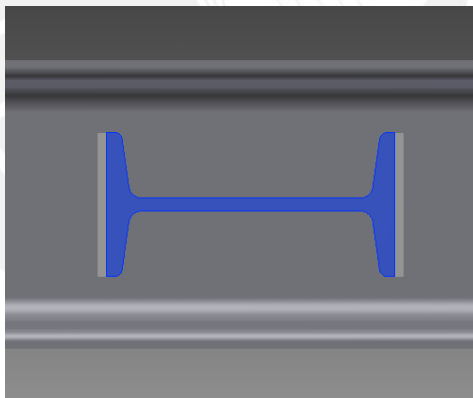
Disposición de los cordones de soldadura en el perfil I.
